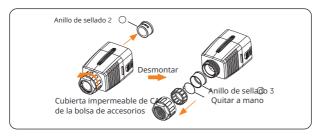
7 Desmontaje de la cubierta impermeable de CA
